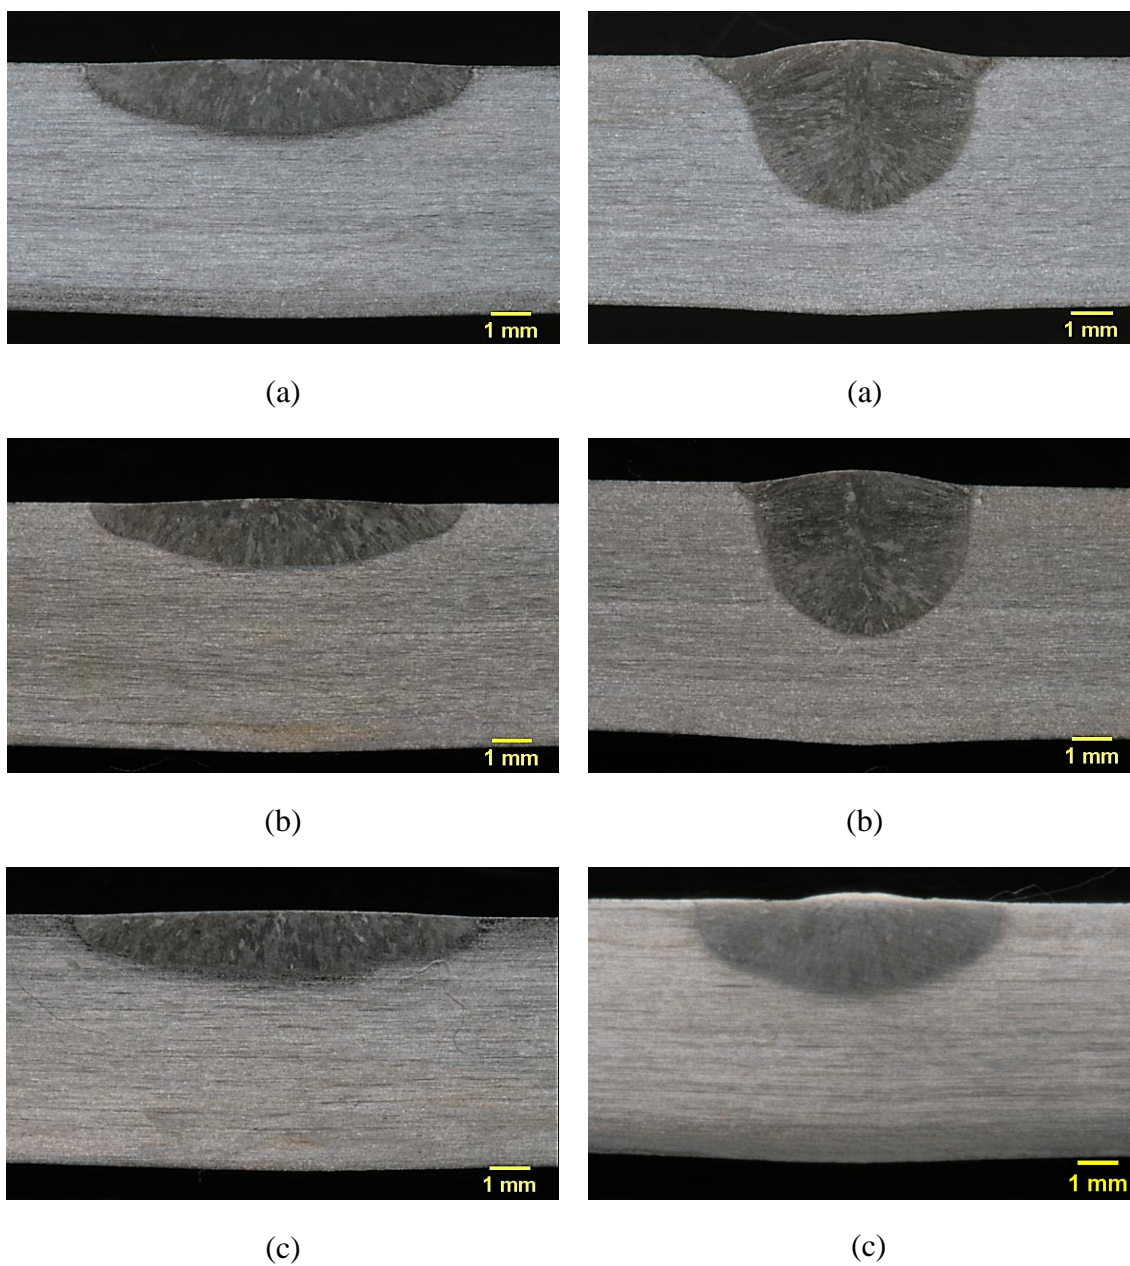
Aspecto dos cordões de solda dos testes: (a) C30/1; (b) C60/0; (c) S30/1; (d) S60/0; (e) A30/1; (f) A60/0.
